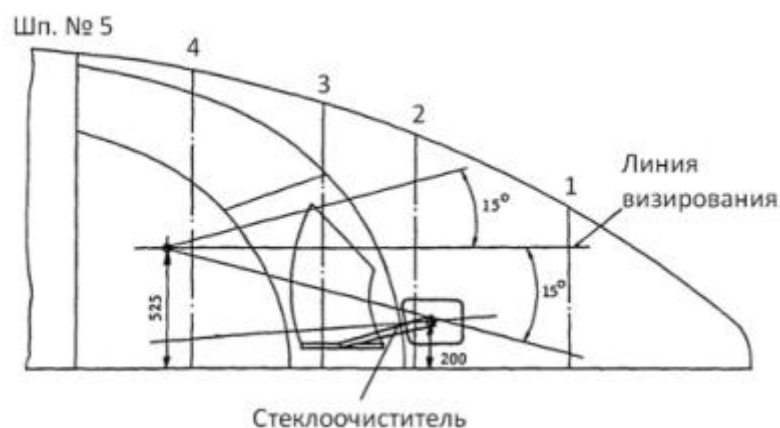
Омітальний діапазон поверхні лобового скла
